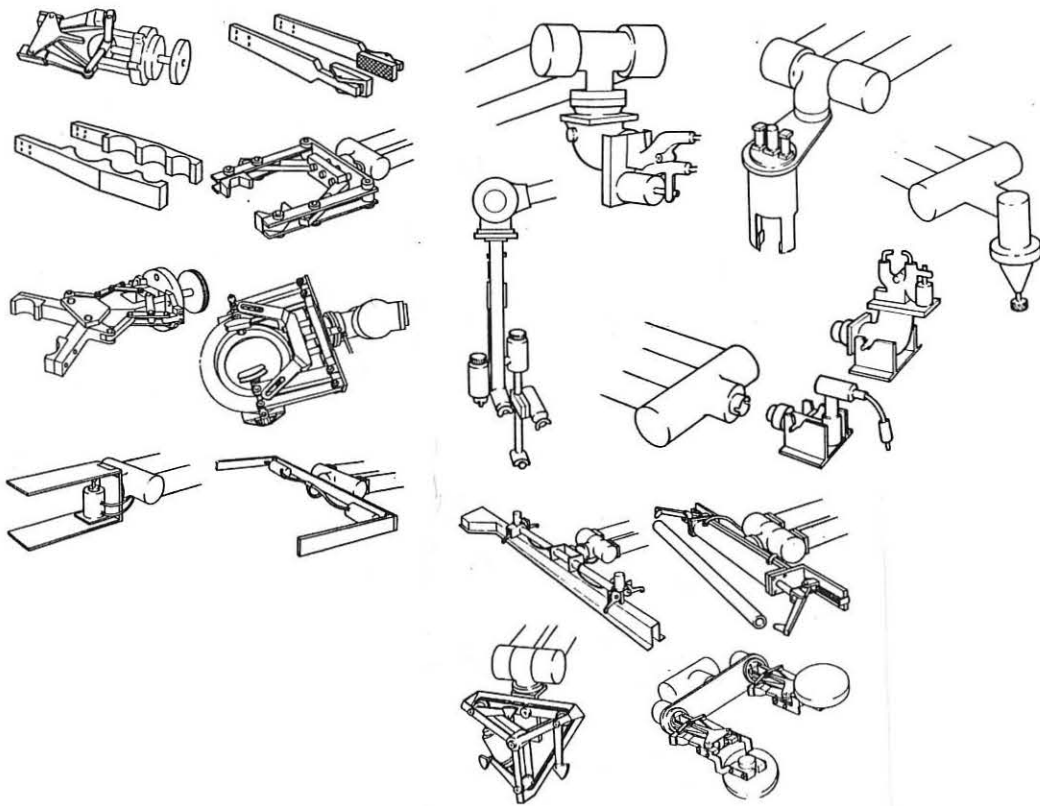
Beispiele für Greifer und Werkzeuge (Engelberger)
